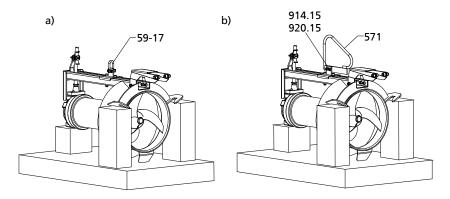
Amaline con: a) Grillete 59-17 b) Estribo 571
